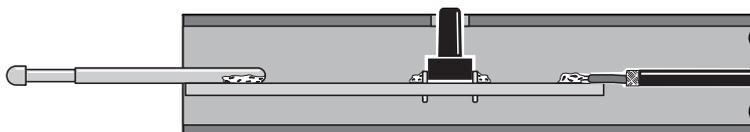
insertad el pin del botón en el pequeño orificio que tiene el tubo. Soldado el electrodo tal cual el dibujo, veréis que sobresaldrá unos 23 mm del tubo.
